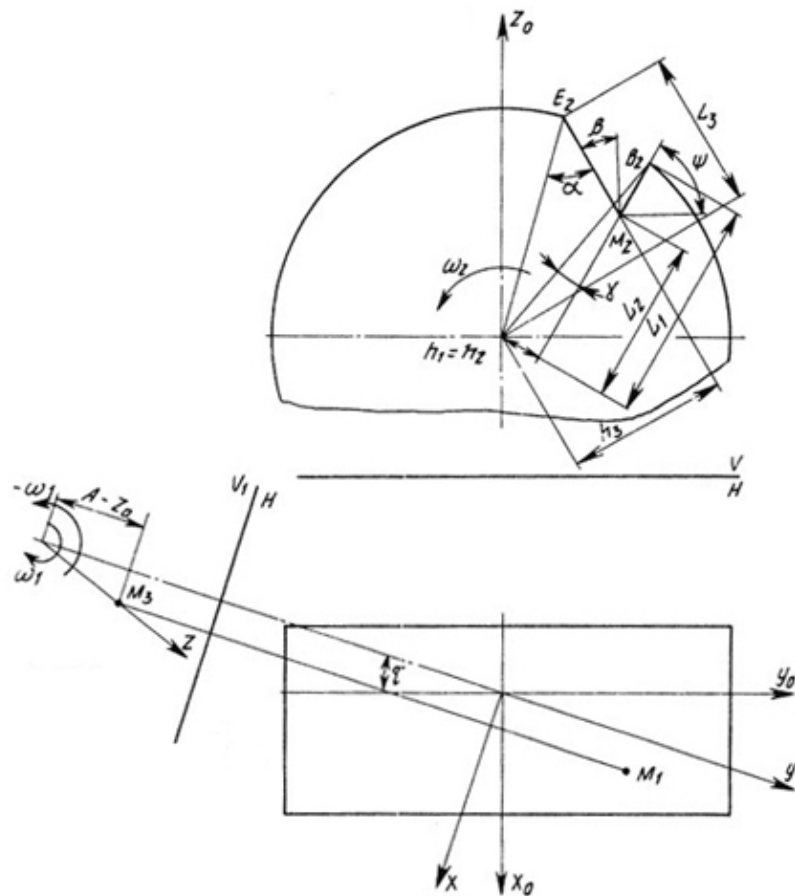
Схема нарізування дисковою обкатною фрезою храпового колеса [38,80]
